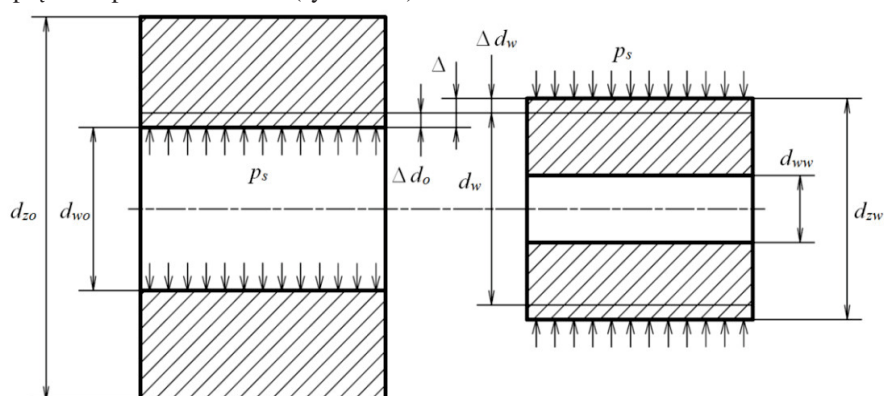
Połączenie wciskowe: a) przed montażem, b) po montażu [16]
